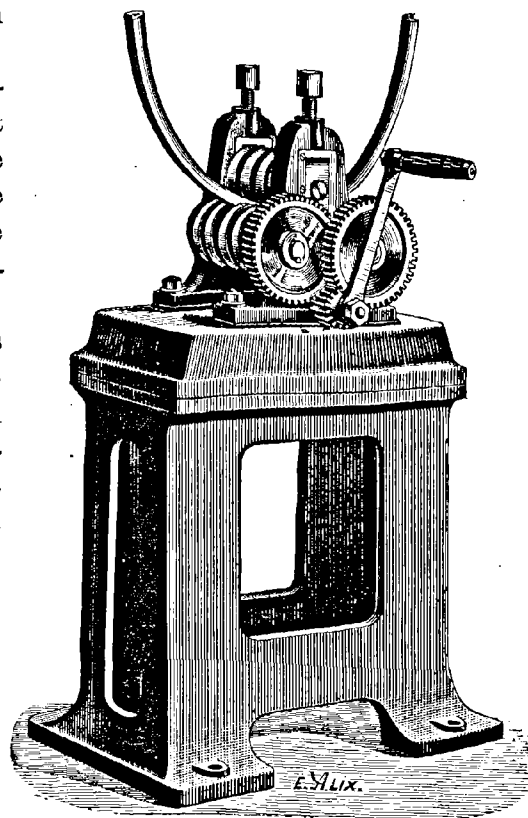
Machine à cintrer pour jantes de vélocipèdes et petits tuyaux.
